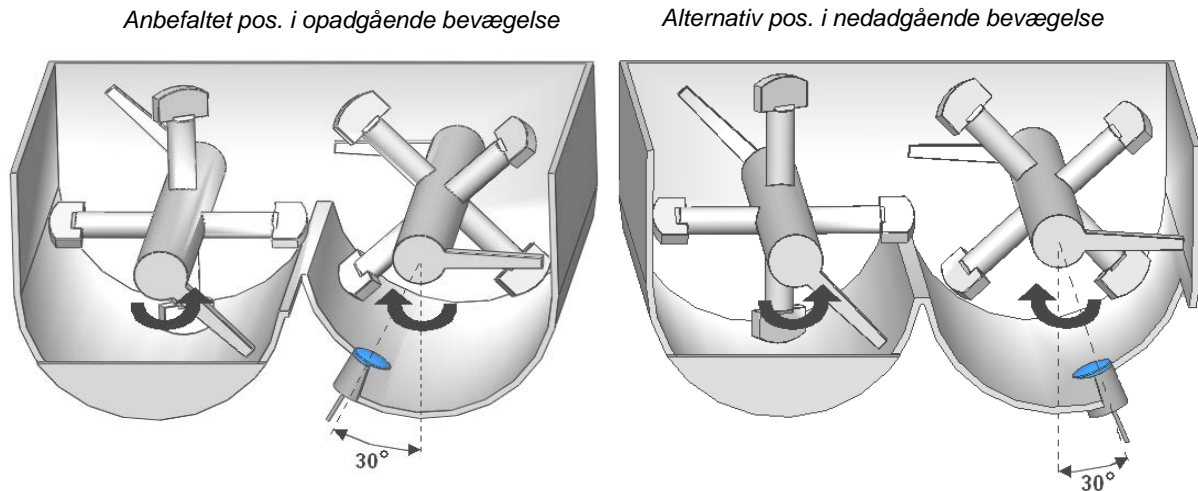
Placering af sensor i horisontal aksialblander eller gennemstrømningsblander
